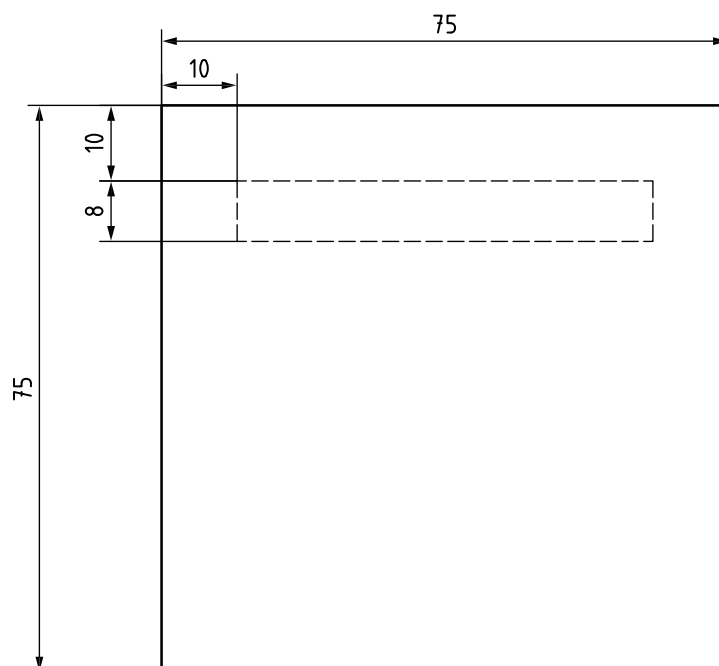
Surface support des échantillons sur la plaque d'écoulement
